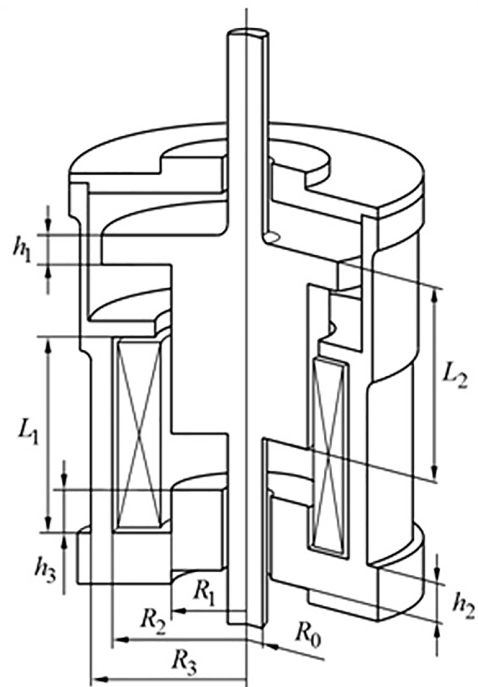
Конструктивные части и геометрические размеры линейного электромагнитного двигателя пресса
